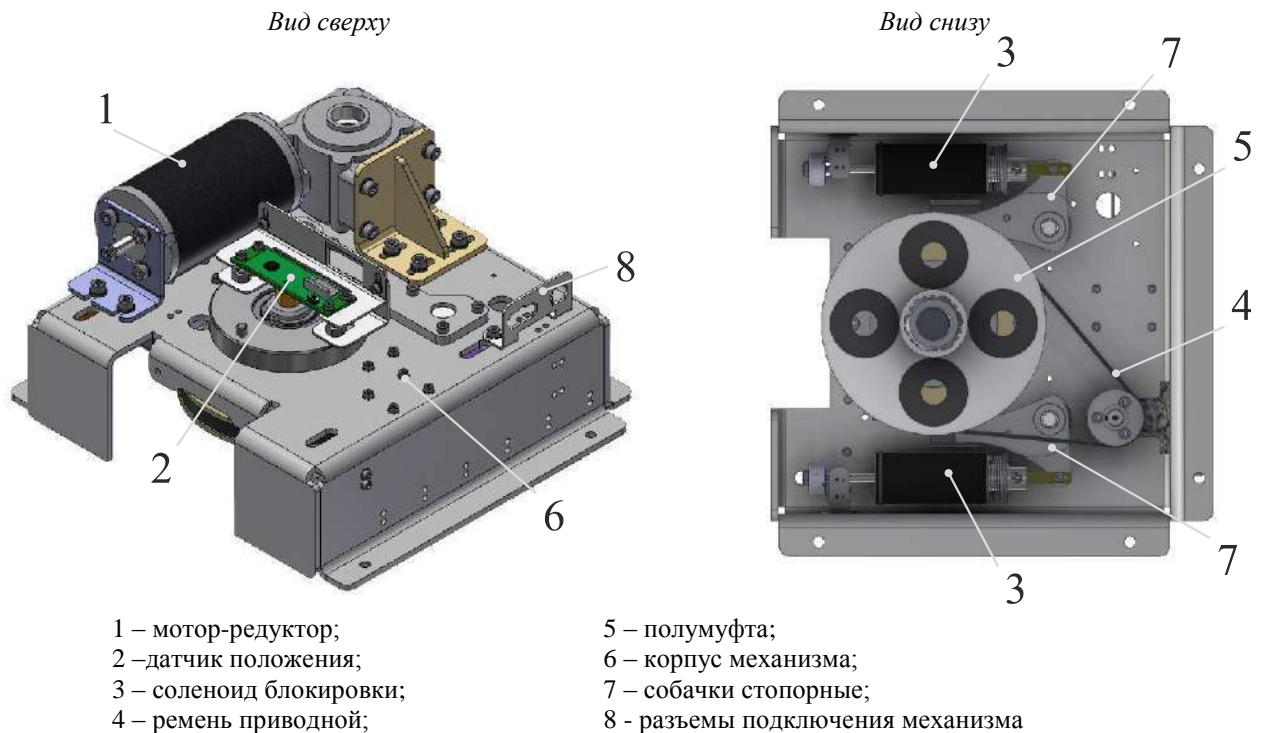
Общий вид и конструкция механизмов калитки и ротора турникета «BICYCLONE-L»
